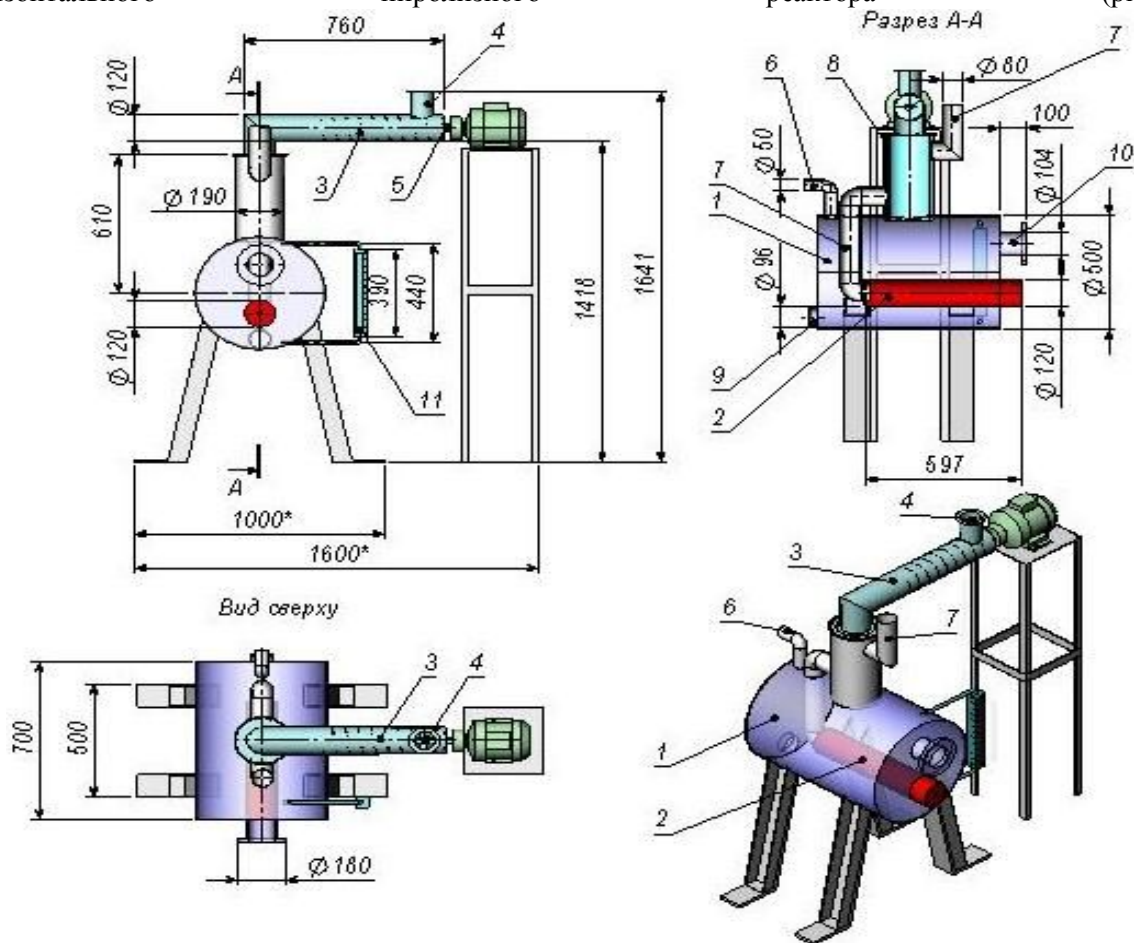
Пиролизный реактор: 1-пиролизная камера; 2-камера сгорания; 3-приемный бункер для сырья; 4-люк для приемной камеры; 5-шnek для подачи сырья; 6-труба для выхода пиролизной паро-газовой смеси; 7-труба для отходящего газа; 8-рекуперативная рубашка; 9-люк для удаления кокса; 10-люк для смотра внутри пиролизной камеры; 11-уровномер для пиролизной жидкости.
